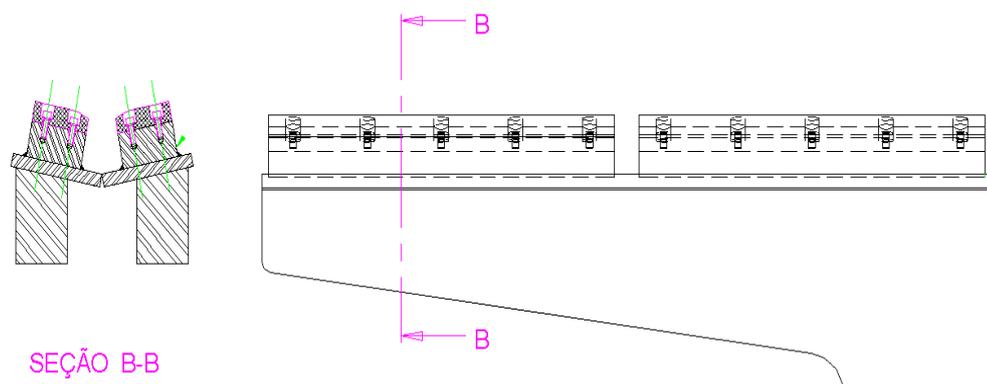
Carro elevador modificado com dispositivos de tarugos de aço
